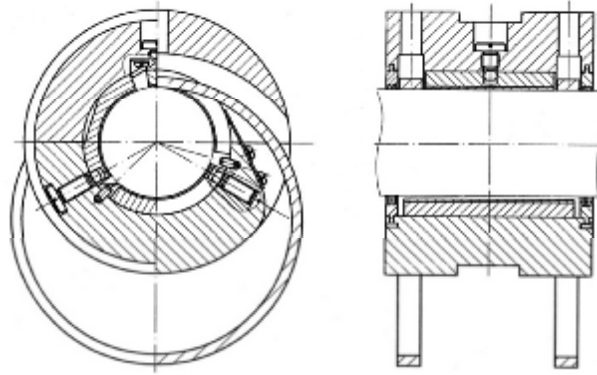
Демпферный подшипник ТРИЗ® типа ПД с картерной смазкой
